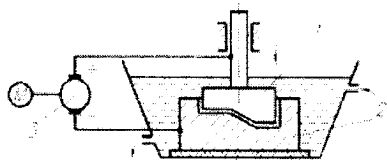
Схема електроімпульсної обробки: 1- інструмент-анод;
